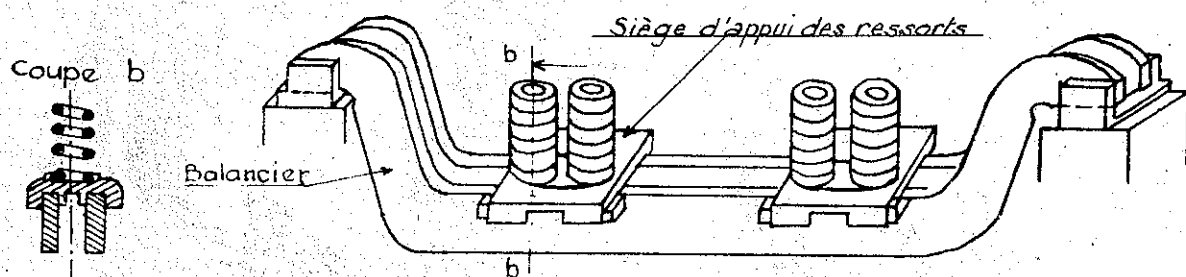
Vue cavalière d'un montage "balanciers" de suspension primaire de bogie de loc 040 DE 500.
